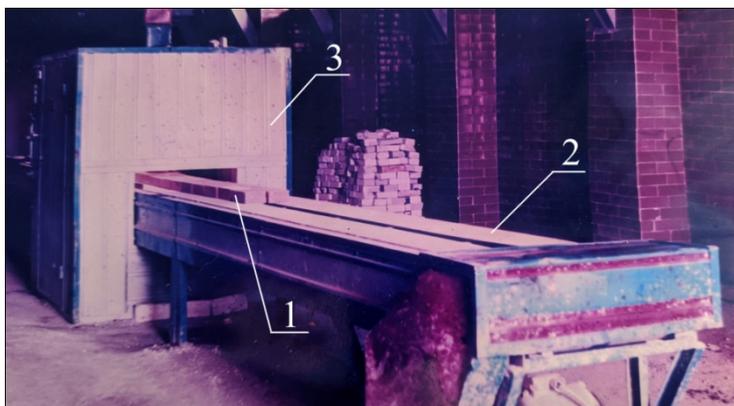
Плазменная установка для обработки кирпича: 1 - обрабатываемое изделие; 2 - конвейер подачи обрабатываемых изделий; 3 - рабочая зона, огороженная защитным корпусом с подведенной системой вентиляции, внутри которой расположен плазменный генератор
